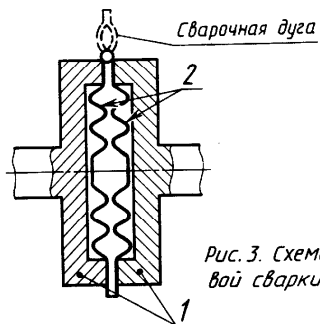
Схема аргонодуговой сварки мембраны
